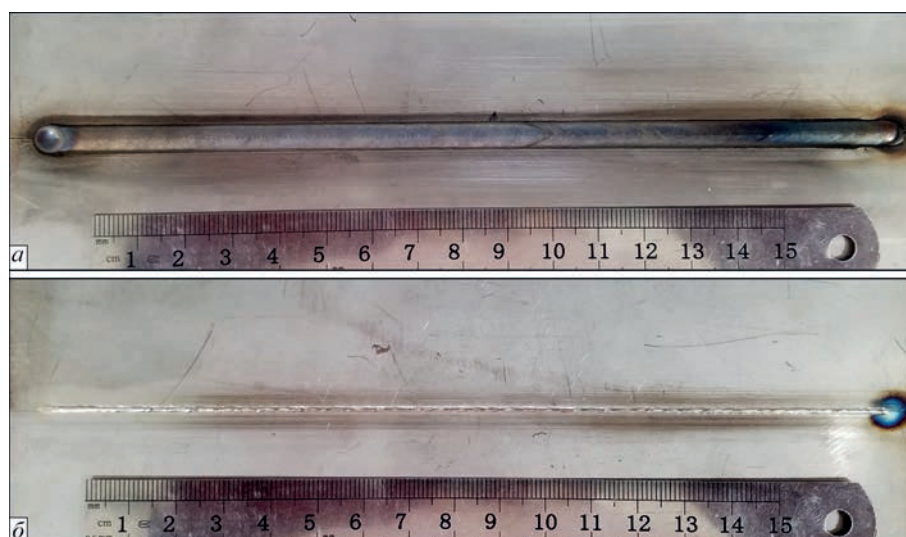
Внешний вид пластин стали SUS304 ( $\delta = 3,0$  мм), сваренных встык без зазора между кромками лазерно-микроплазменным способом (мощность излучения  $P = 1,2$  кВт, сварочный ток  $I = 80$  А, напряжение  $U = 28$  В, скорость сварки  $v = 40$  м/ч): лицевая (а) и обратная (б) стороны
